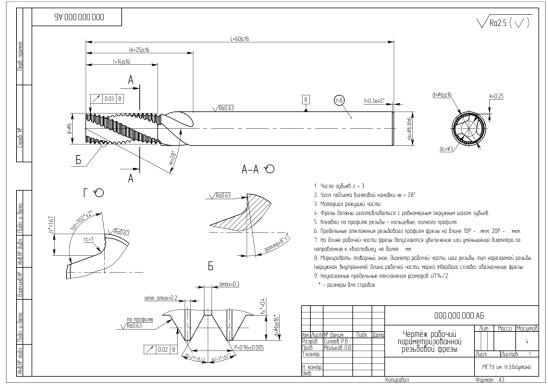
Рабочий чертёж резьбовой гребенчатой фрезы.
